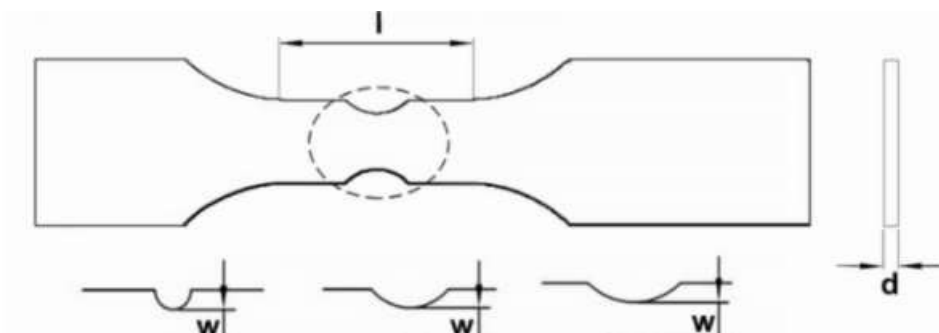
Dimensions standardisées d'une éprouvette entaillée
